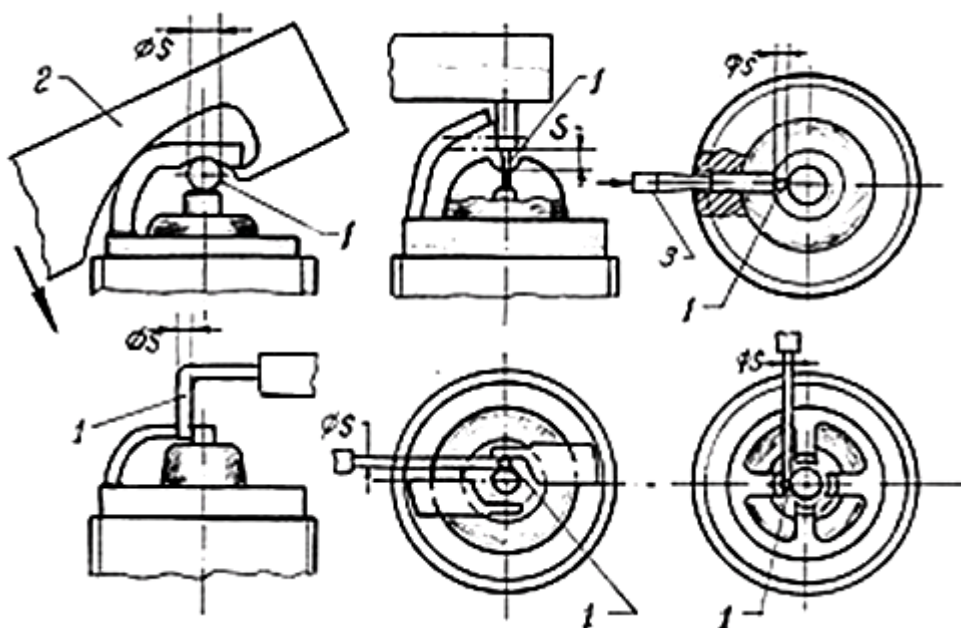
Проверка и установка искрового промежутка свечей:
